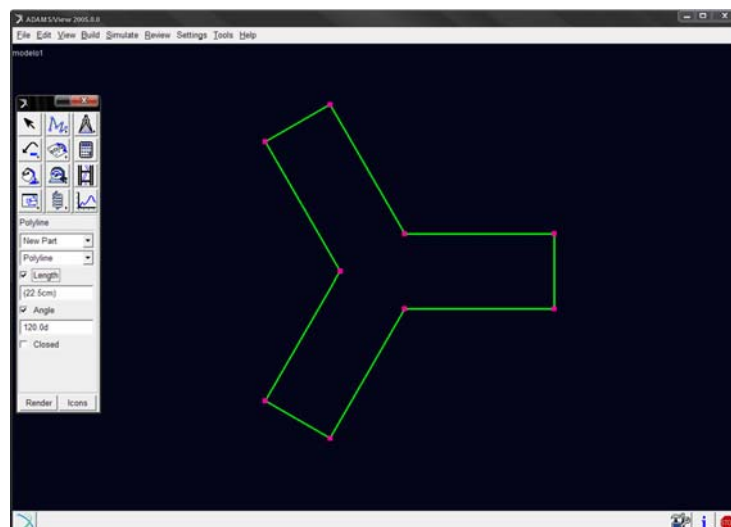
Perfil rotor del rodamiento de 3 bolas
